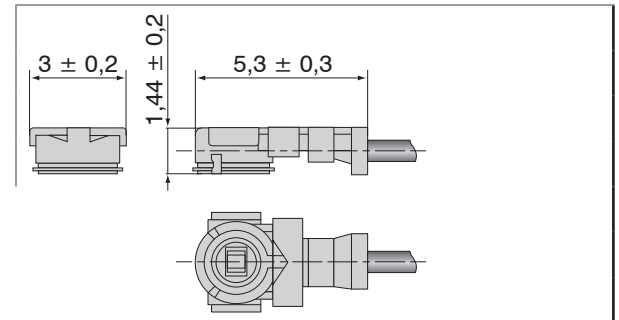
Dessin coté câble du capteur, dimensions indiquées en mm, pas à l'échelle
